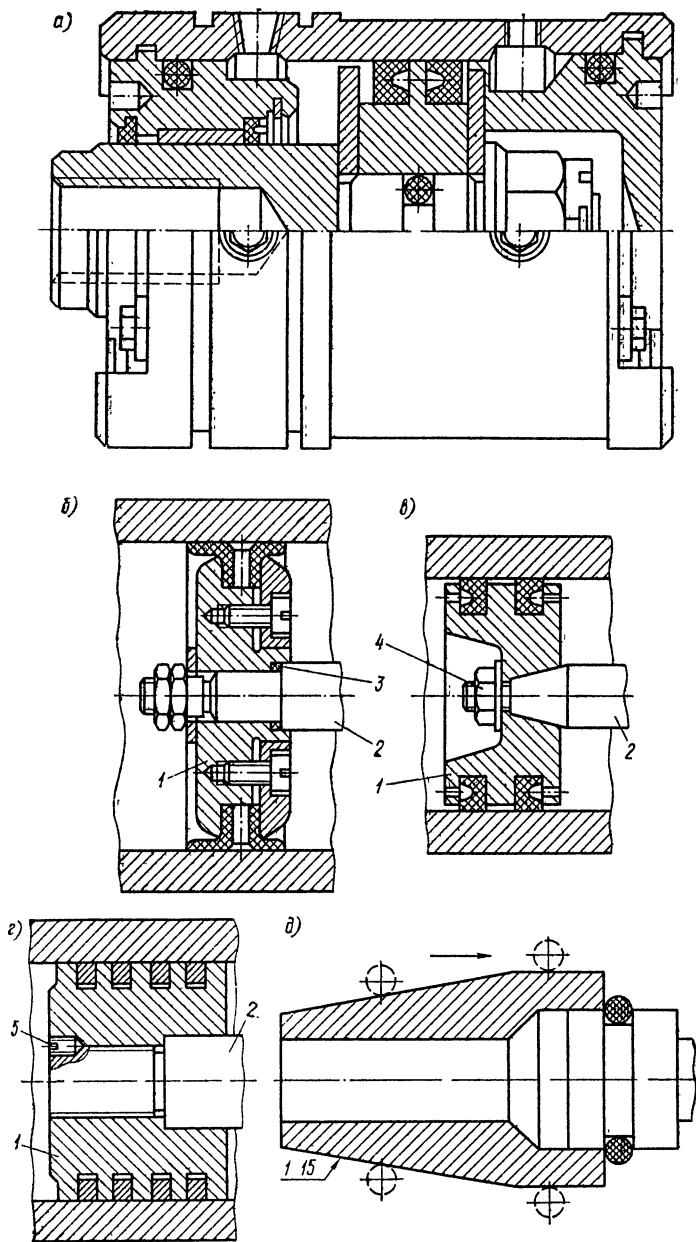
Общий вид гидроцилиндра и способы установки поршней
